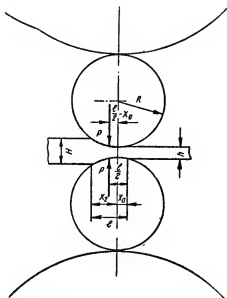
Схема прокатки при сплюснутых рабочих валках
